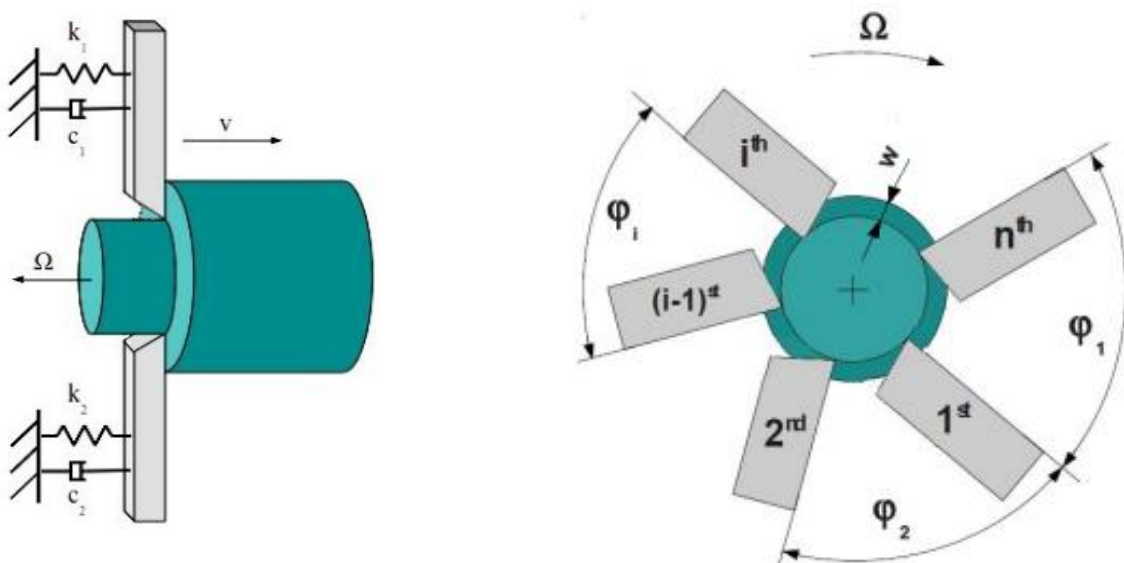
Механічна модель багаторізцевої системи токарного оброблення [12]
